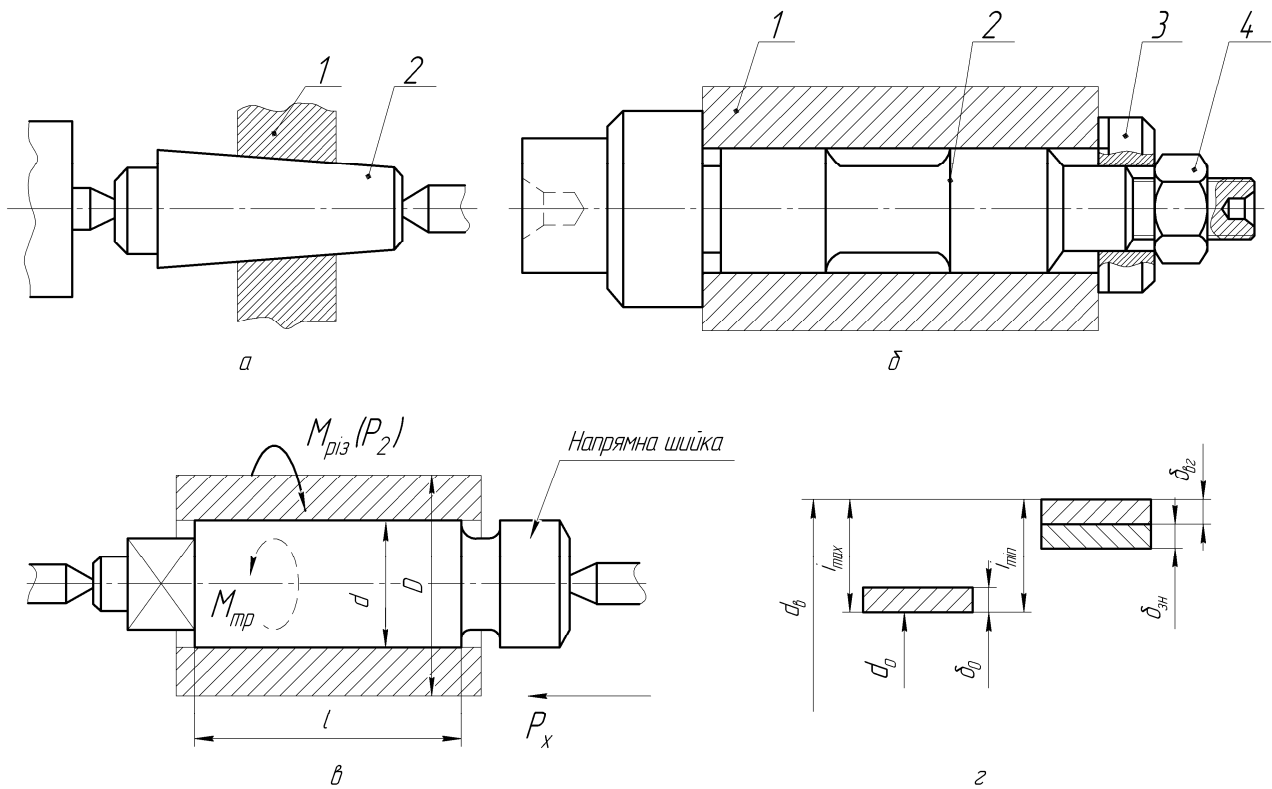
Схеми й параметри різних видів центричних оправок для кріплення циліндричних заготовок у центрах на токарному верстаті: *a* – конусна для високої точності центрування; *б* – оправка для розміщення заготовки з гарантованим зазором; *в* – під запресовування; $M_{тр}$ – момент тертя, $M_{рез}$ – момент різання, P_x – рушійна сила (сила опору подачі); i – розташування полів допусків з'єднання «оправка – заготовка»; $\delta_{зн}$ – допуск на зношування оправки; $\delta_{вг}$ – допуск на виготовлення оправки; i_{min} , i_{max} зазор між деталлю та оправкою; δ_0 – допуск на отвір; d_0 – діаметр отвору; d_b – діаметр вала; 1 – деталь; 2 – оправка; 3 – шайба; 4 – гайка
